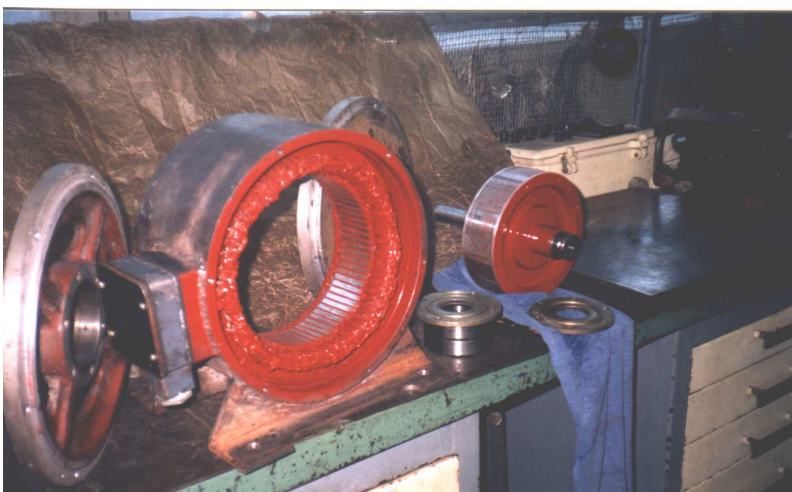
Основные элементы опытного образца СГПМ 2,5-375 перед сборкой генератора
